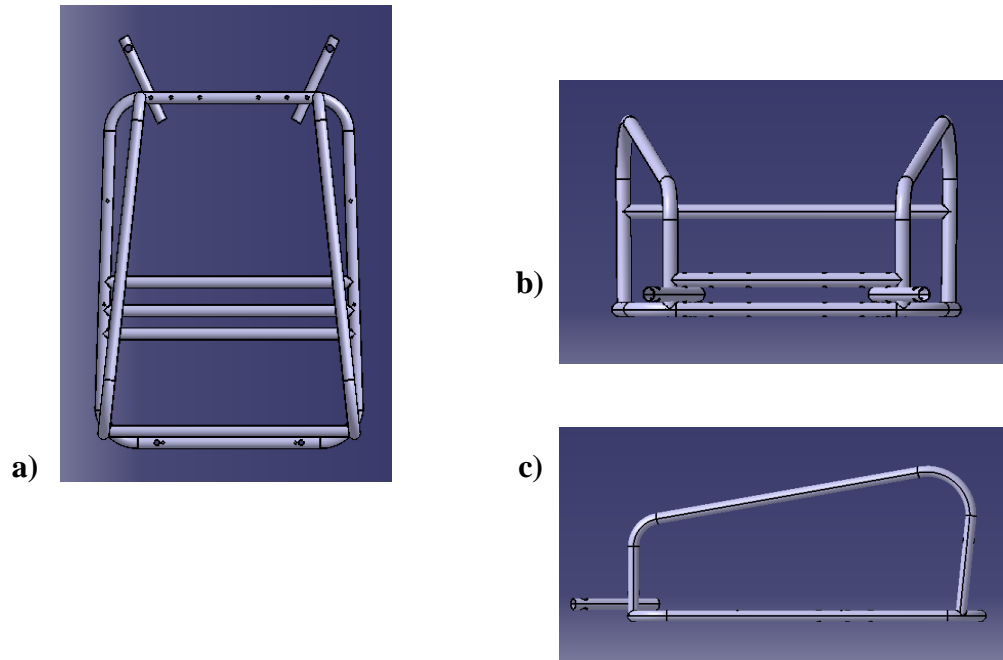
a) Vista superior. b) Vista frontal. c) Vista lateral.
